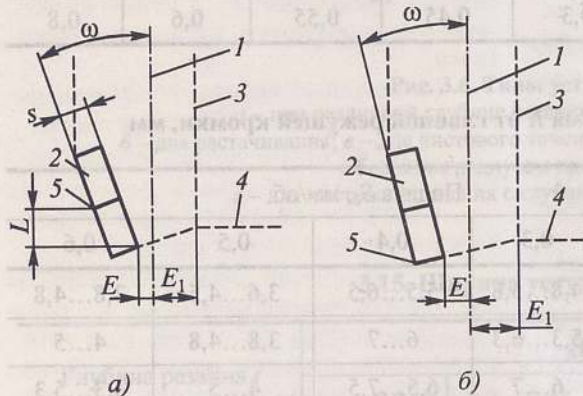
Схема определения смещения паза под СМП: а – расточной инструмент; б – торцовая фреза; 1 – ось инструмента; 2 – СМП; 3 – державка; 4 – торец корпуса инструмента; 5 – вершина СМП
